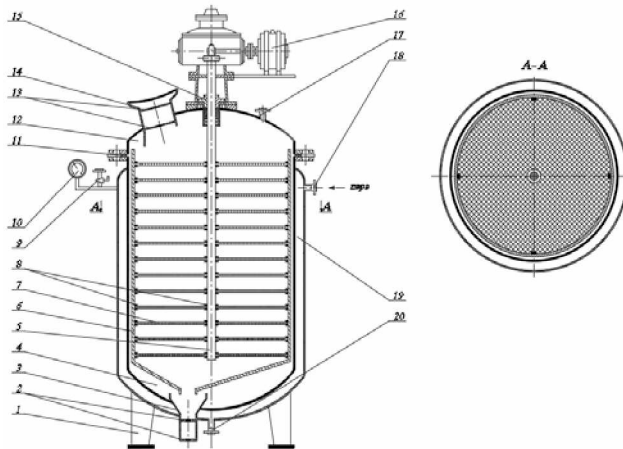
Вібраційна вакуумна сушарка безперервної дії для сушіння овочевої сировини: 1 — опори; 2 — запірний клапан; 3 — горловина; 4 — робоча камера; 5 — робочий вал; 6 — корпус для лотків; 7 — лотки для продукту; 8 — кріпильні елементи; 9 — клапан для видалення надлишкового повітря; 10 — манометр; 11 — затискач; 12 — кришка апарата; 13 — дозуючий клапан; 14 — завантажувальний бункер; 15 — ущільнювач для герметизації; 16 — віброгенератор; 17 — патрубок для видалення повітря; 18 — патрубок для подачі теплоносія; 19 — парова оболонка; 20 — патрубок для зливу теплоносія
